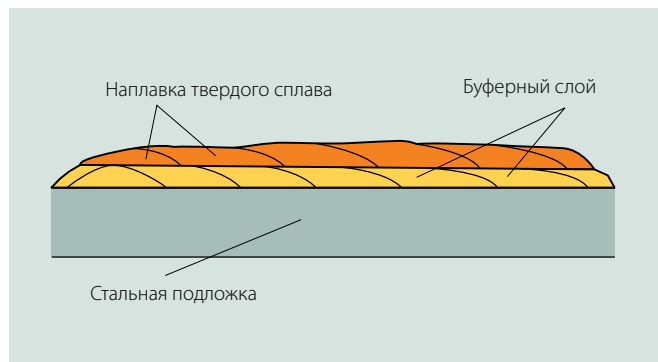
Образец порядка нанесения сварных швов с использованием электродов для буферного слоя и наплавки твердого сплава
